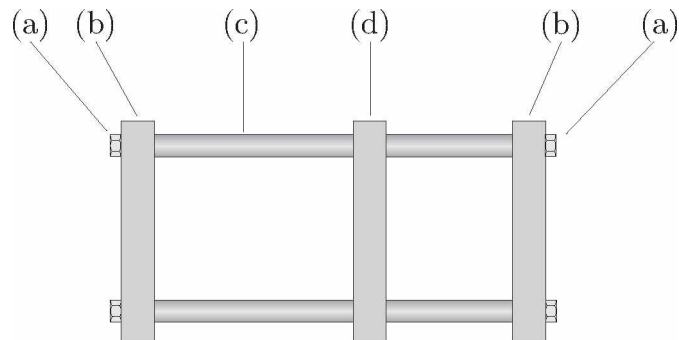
Säulengestell: Das Säulengestell besteht aus den Komponenten (a) Schraubenbefestigung durch Schraubenmutter; (b) Befestigungsplatte; (c) Säulen; (d) verfahrbare Zwischenplatte.
